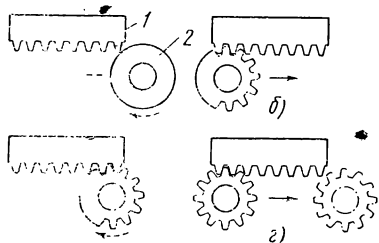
Схема нарезания зубьев зубчатой гребенкой:
